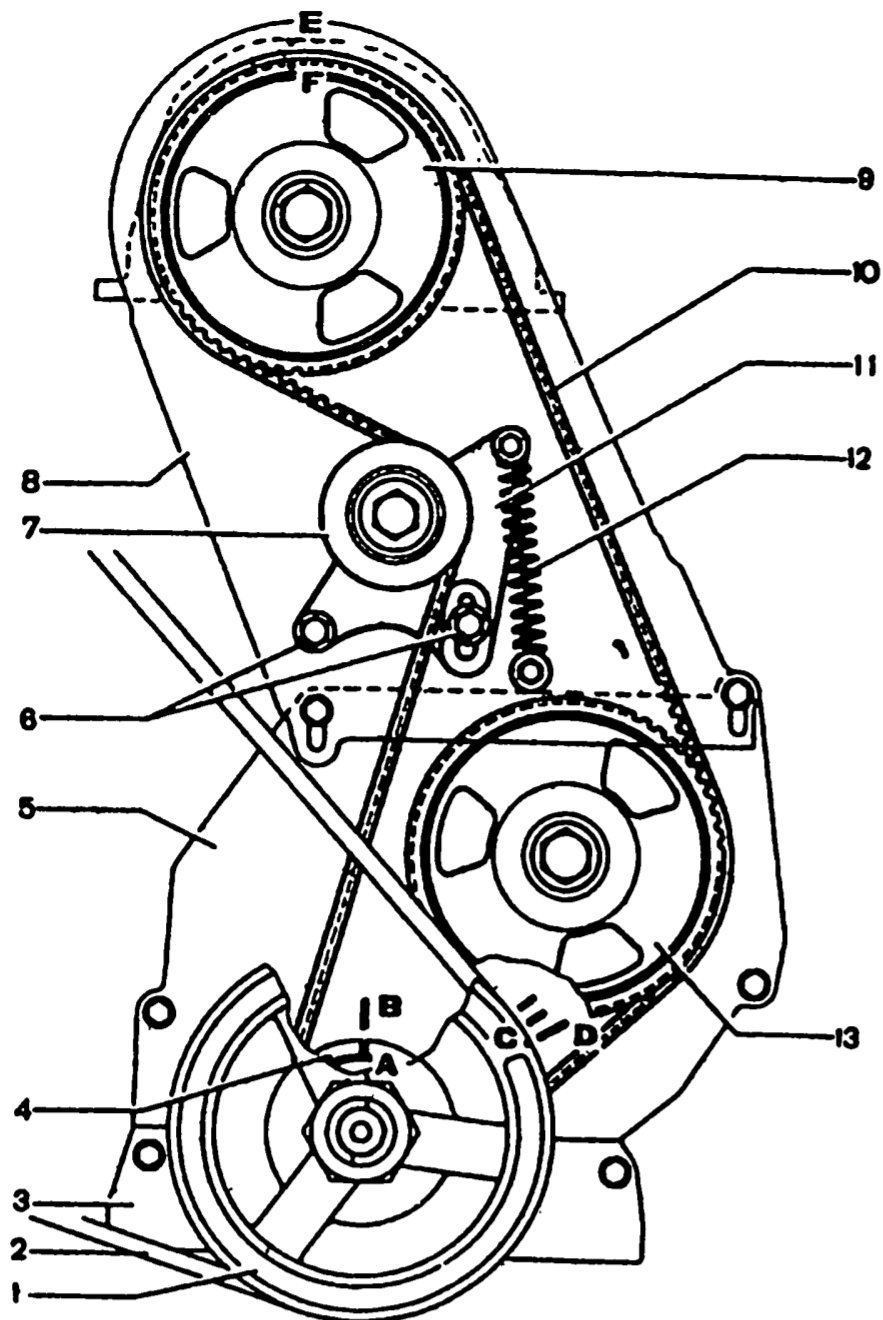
Схема привода распределительного вала: 1 - шкив коленчатого вала; 2 - ремень привода вентилятора; 3 - нижняя защитная крышка; 4 - зубчатый шкив коленчатого вала; 5 - средняя защитная крышка; 6 - болты крепления кронштейна натяжного ролика; 7 - натяжной ролик; 8 - верхняя защитная крышка; 9 - шкив распределительного вала; 10 - зубчатый ремень; 11 - кронштейн натяжного ролика; 12 - пружина кронштейна; 13 - шкив валика привода масляного насоса; А - Метка на зубчатом шкиве коленчатого вала; В, D - метки ВМТ на крышке привода распределительного вала; С - метка на шкиве коленчатого вала; Е - метка на крышке головки цилиндров; F - метка на шкиве распределительного вала
